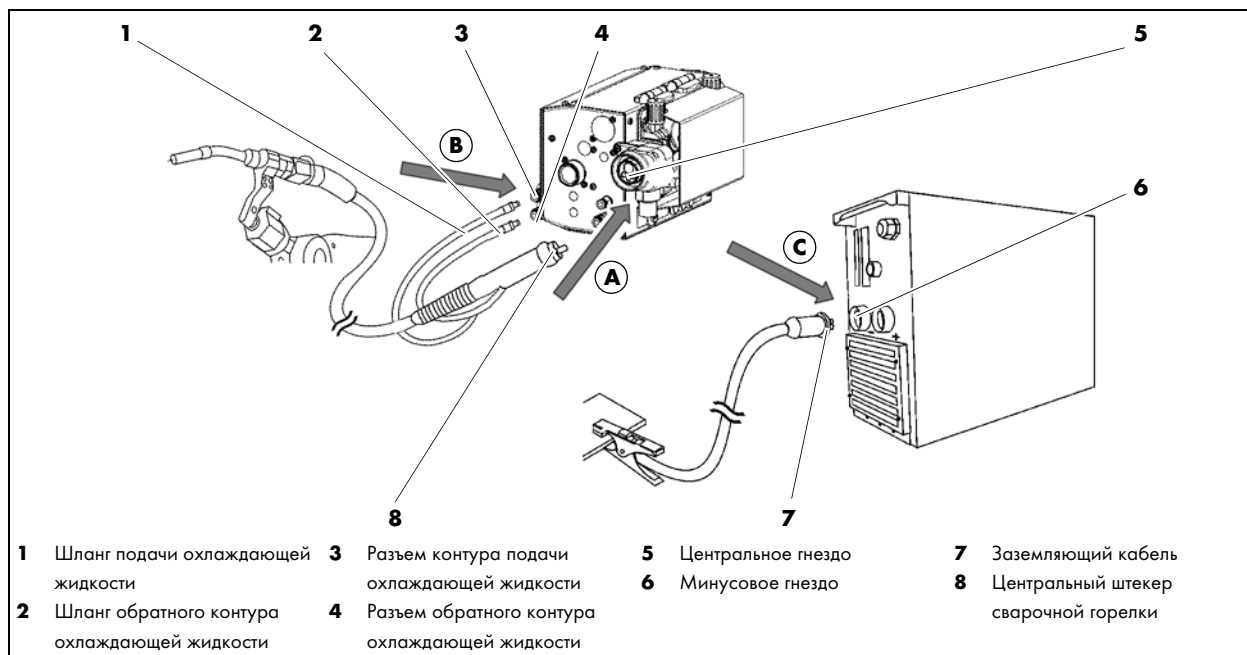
Шланговый пакет сварочной горелки (центральный евроразъем) iROB-feed 22
